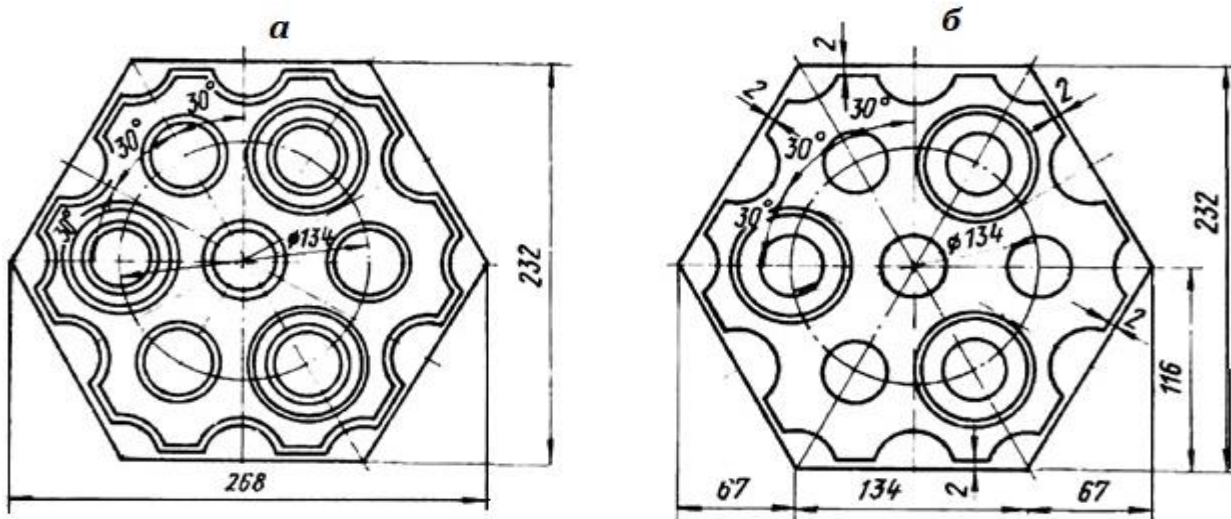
Шестигранный насадочный блок с 12 круглыми каналами: а – вид снизу; б – вид сверху
